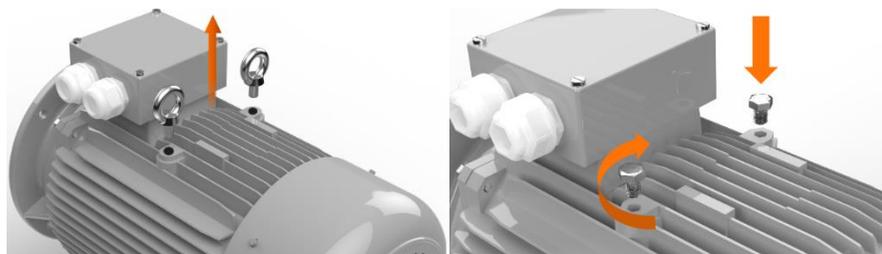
Austausch von Ringschrauben durch Sechskant-Schrauben bei Motoren mit erhöhter IP – Schutzart und Ex – Motoren
